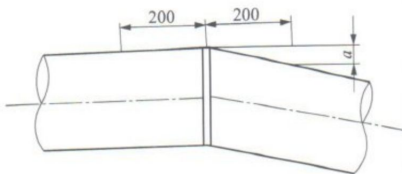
管道焊接角变形折口偏差示意图
